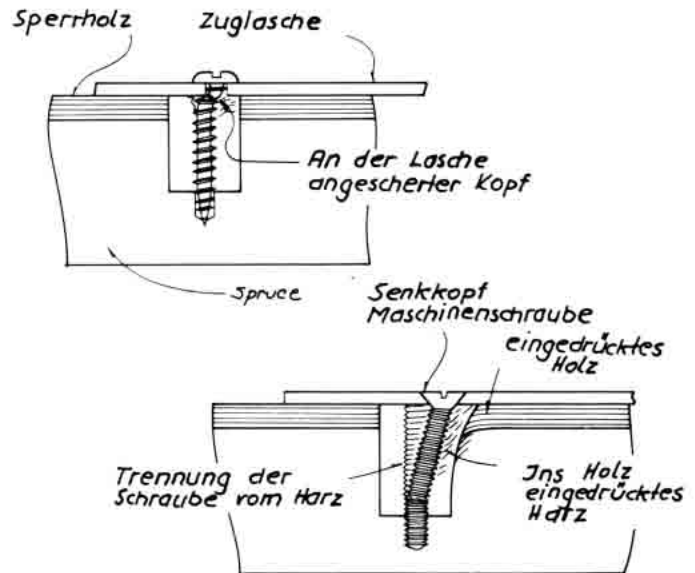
Versagensformen von auf Schub beanspruchten selbstschneidenden Schrauben und Senkkopf-Maschinenschrauben.
